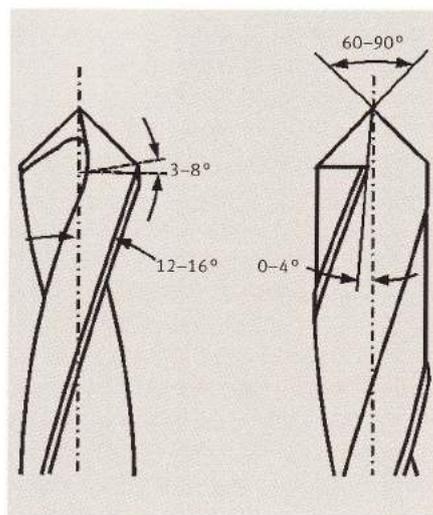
Правильная заточка сверла из быстрорежущей стали для обработки материалов PLEXIGLAS® (режущие края должны скреститься, а не резать)
